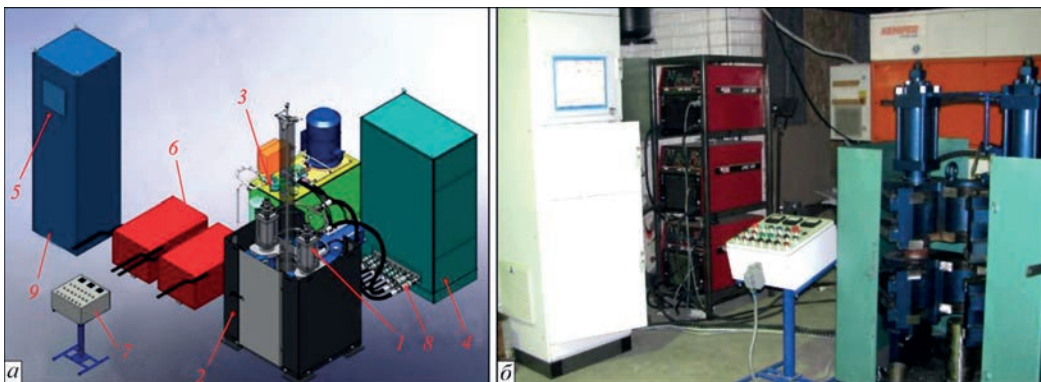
Установка МД205 для зварювання труб: а – склад обладнання; б – машина МД205 на виробництві
